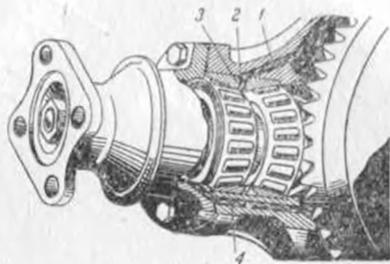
Схема смазки переднего подшипника ведущей шестерни главной передачи:
